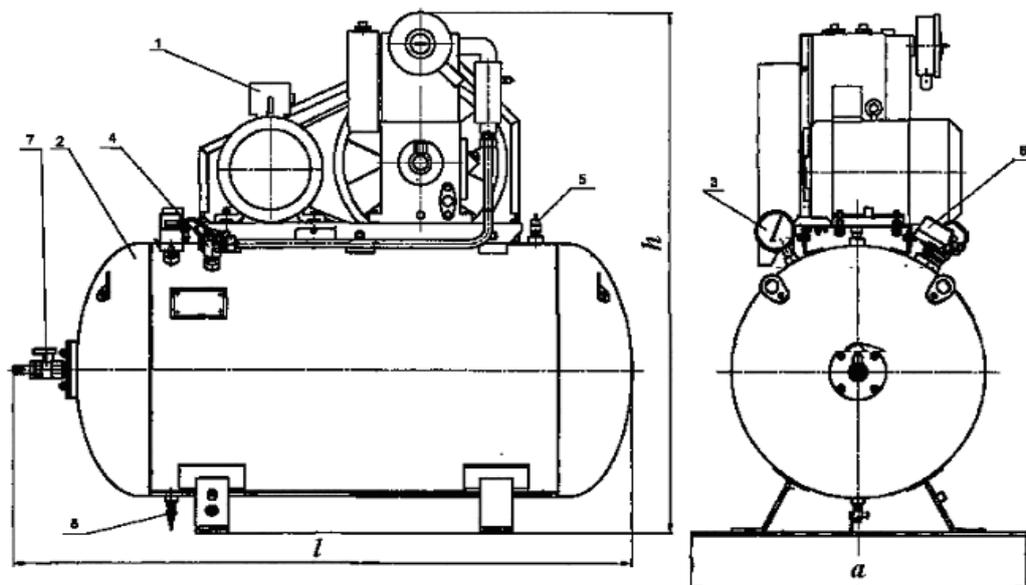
Установка компрессорная ЭПКУ с горизонтальным расположением ресивера
